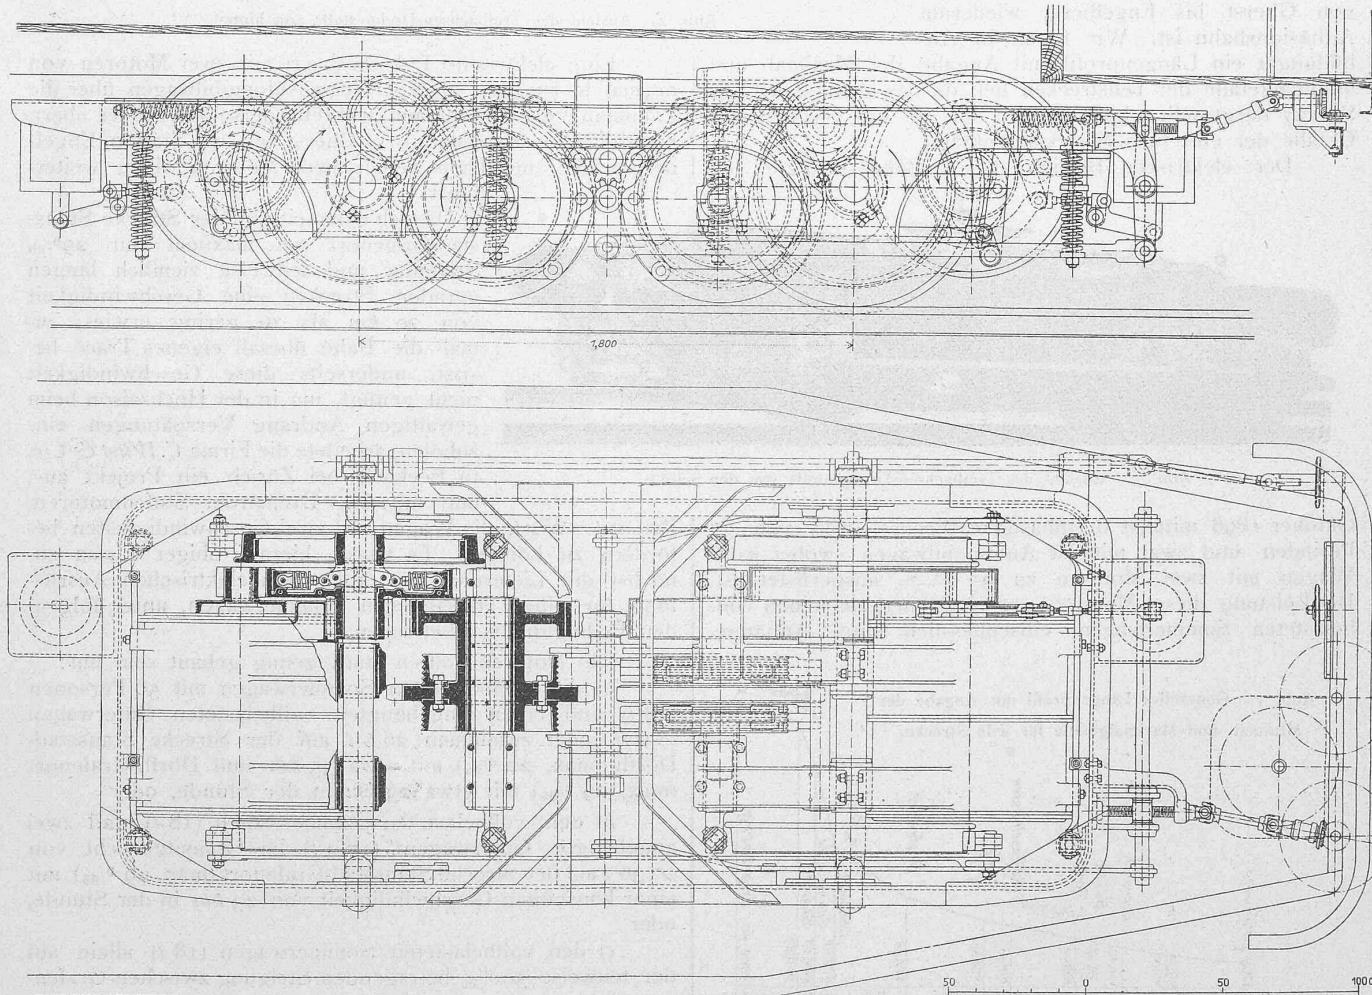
Drehgestell mit dem von C. Wüst & Cie. in Seebach eingebauten elektrischen Antrieb, — Ansicht, Grundriss und Schnitt. — Maßstab 1 : 25.
